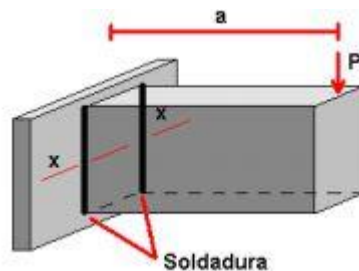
Esquematzación de la soldadura a calcular.
